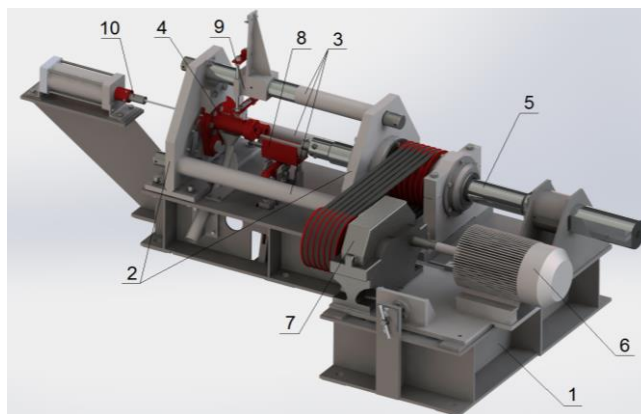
Калибровочный пресс с электромеханическим приводом:
